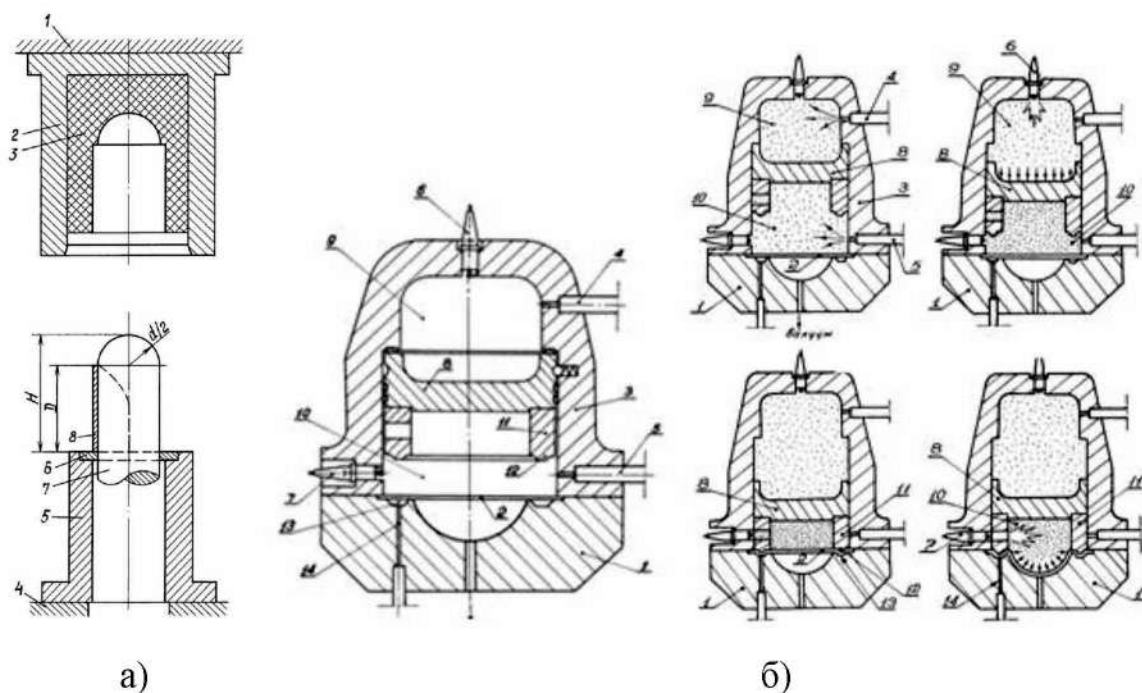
Виготовлення напівсфер: а – в еластичній матриці;
